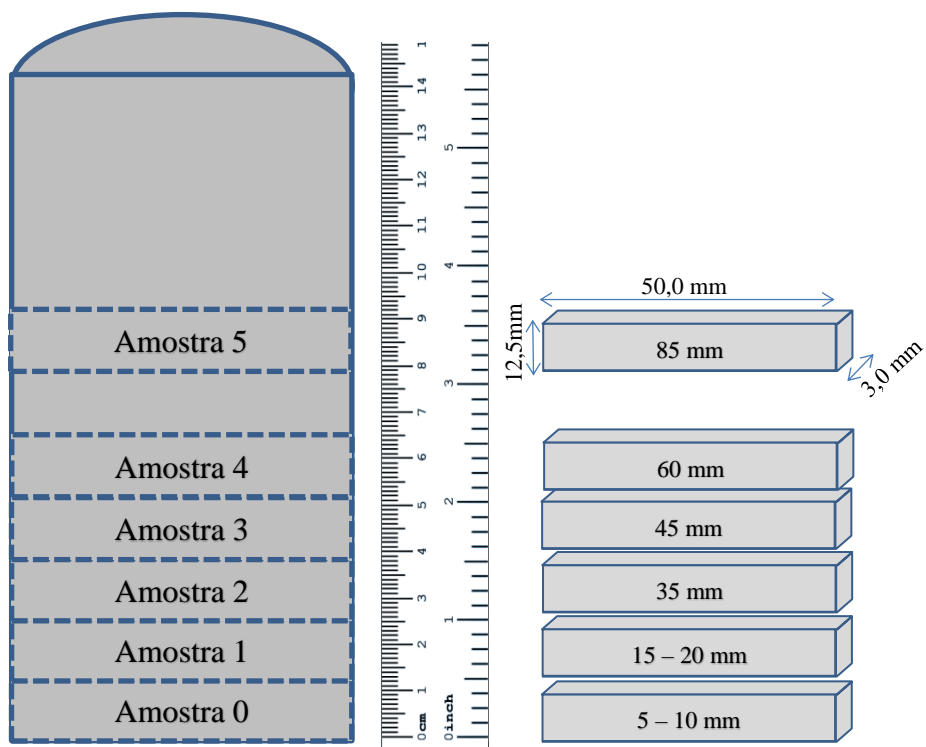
Esquema dos corpos de prova para ensaio de tração retirados do lingote solidificado.
